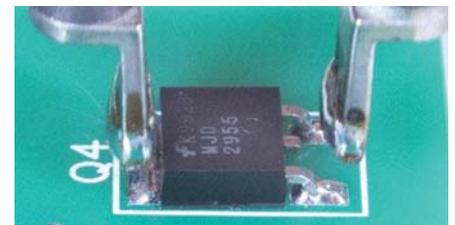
Abaisser les embouts sur le composant et presser la pièce à main.
